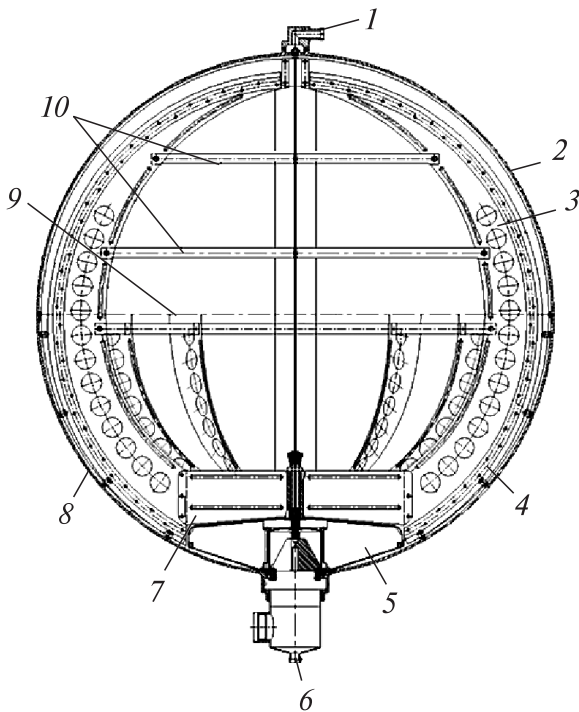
Топливный бак с внутрибаковым устройством капиллярного типа: 1 — корпус бака; 2 — заправочно-сливной штуцер; 3 — наддувный штуцер; 4 — фазоразделительное устройство; 5 — перегородки верхние; 6 — транспортные желоба; 7 — плоские удерживающие перегородки; 8 — конструктивные рамы; 9 — перегородки нижние; 10 — секторные капиллярные элементы
